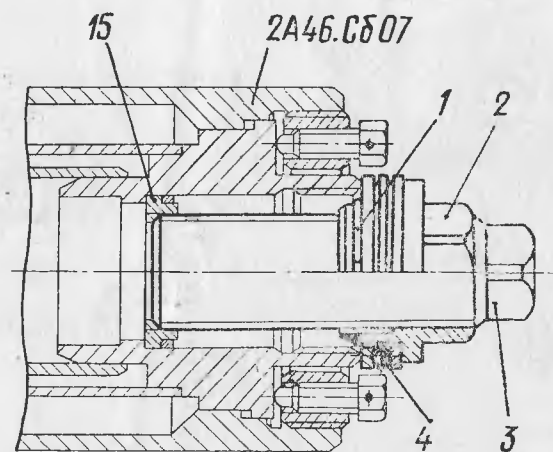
Установка прибора 2А26.Сб 42-9 для вынимания кольца 2А26.07-45:
